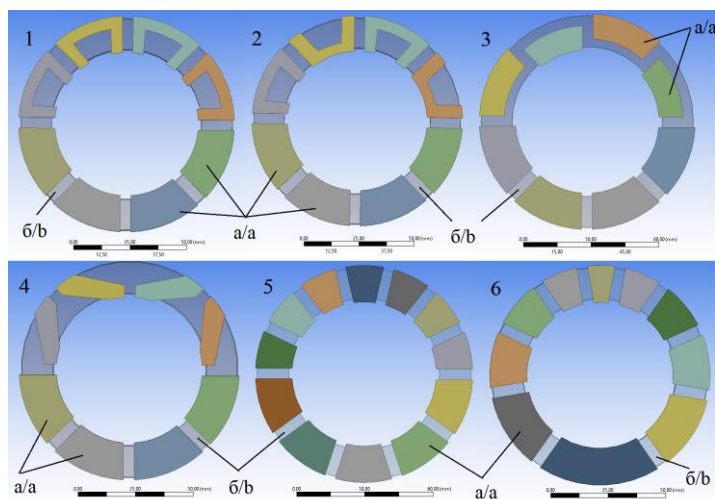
Исследуемые конструкции динамически стабилизирующего инструмента: а – сектора матрицы; б – промывочные каналы;
